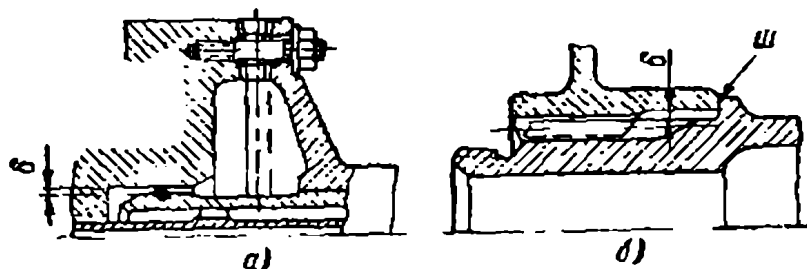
Посадка деталей по цилиндрической поверхности с упором по торцу.
